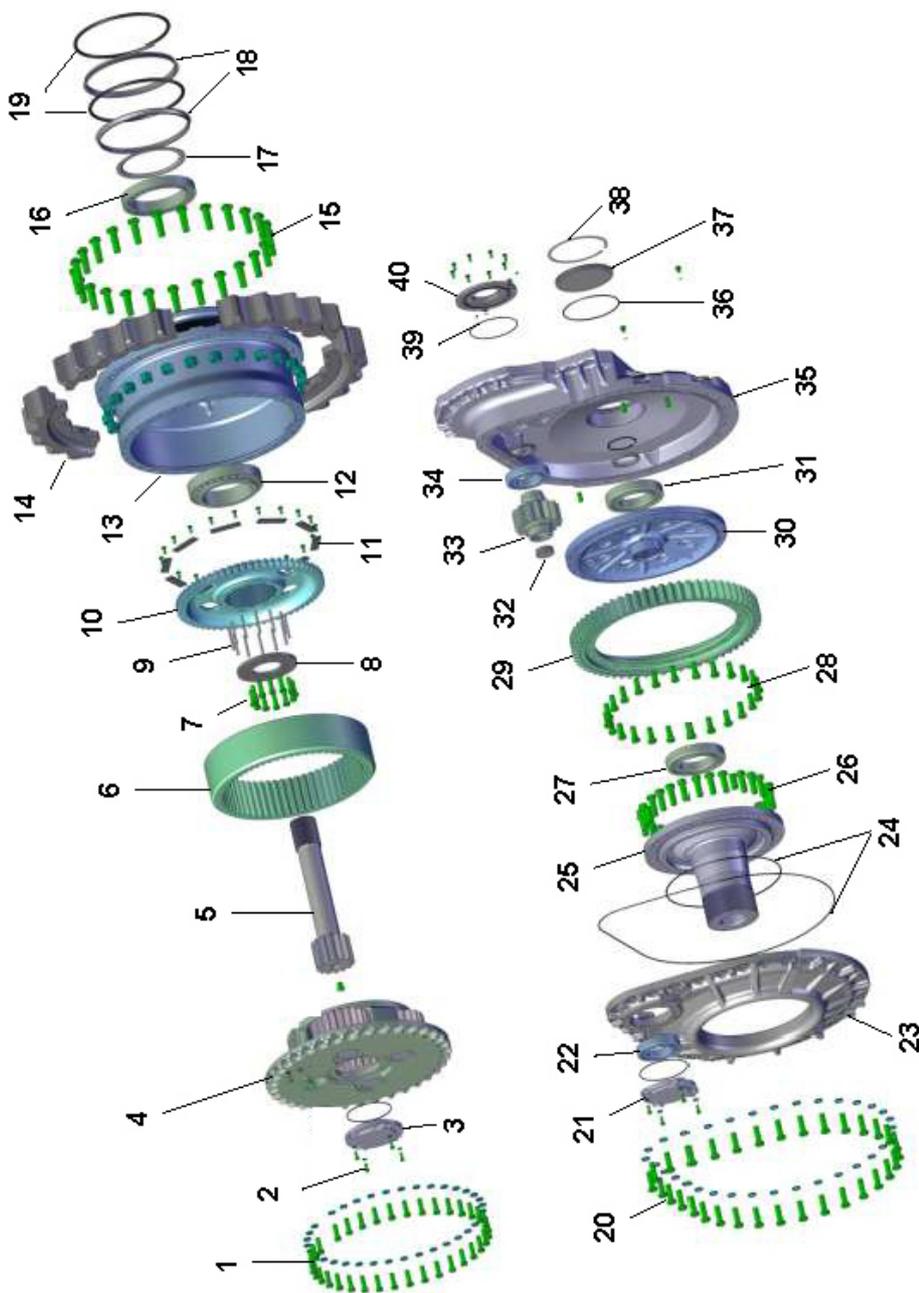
Передаточная бортовая. Схема разборки
